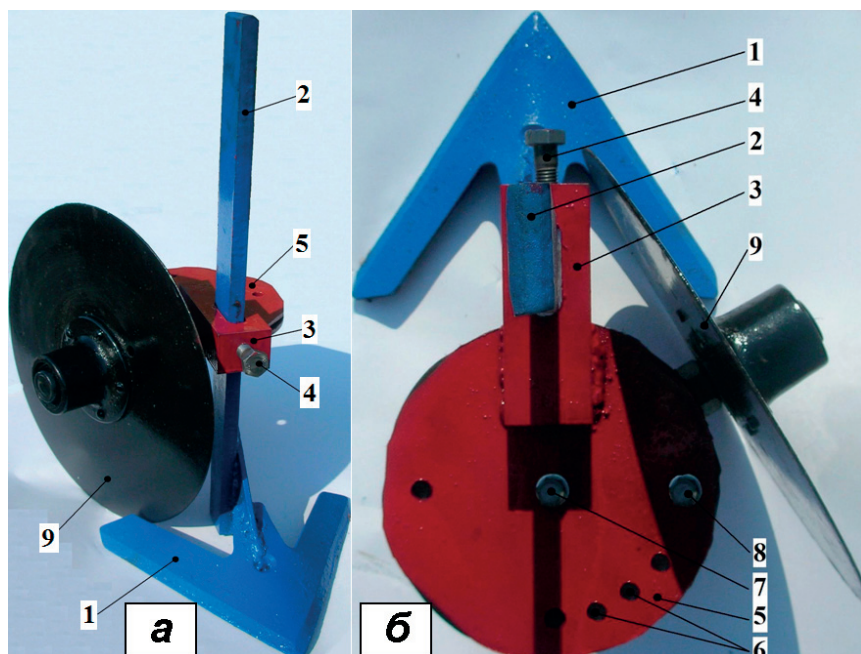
Рабочий орган гребневой сеялки: а – общий вид; б – вид сверху; 1 – стрельчатая лапа; 2 – стойка; 3 – кронштейн; 4 – фиксатор; 5 – регулировочный диск; 6 – отверстия; 7, 8 – болты; 9 – плоский диск
